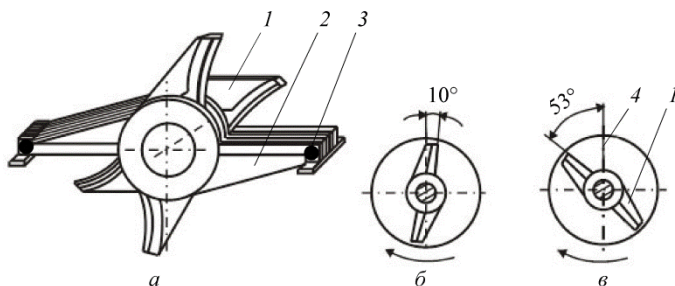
Устройство режущего аппарата второй ступени измельчения:
